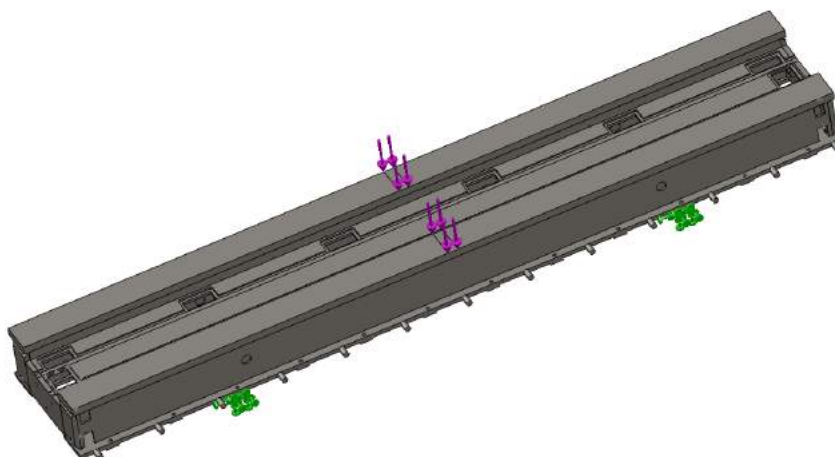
Твердотільна модель зварної станини під супорт
